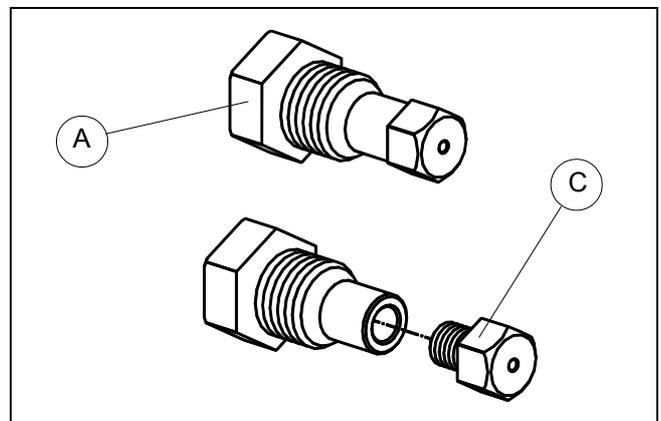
ДЕТАЛЬ ДЕРЖАТЕЛЯ СОПЛА и ОТКАЛИБРОВАННОЕ СОПЛО
